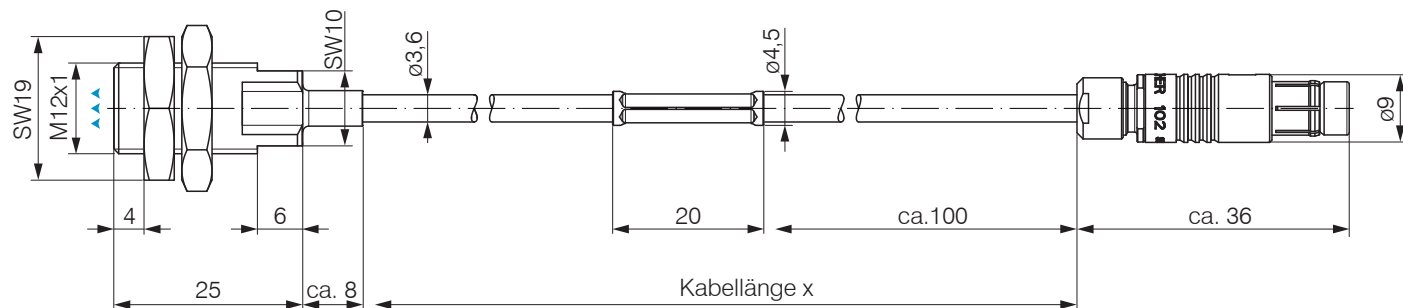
Maßzeichnung Sensoren ES-S2-C-CAx/mB0, Abmessung in mm
